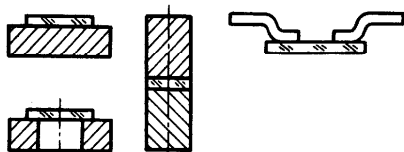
Конструкции соединений полупроводника с металлами, выполненных диффузионной сваркой
